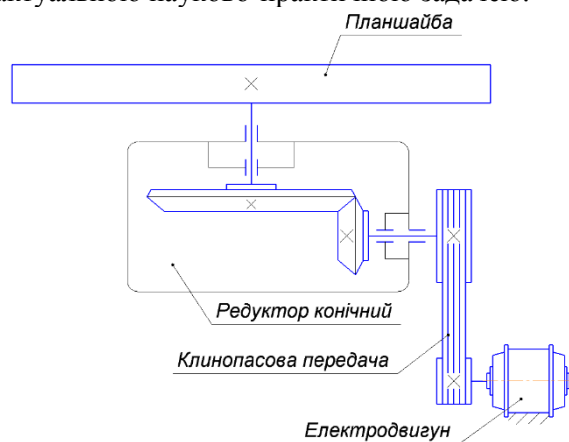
Схема приводу планшайби верстата для шліфування плоских поверхонь скляних плиток
